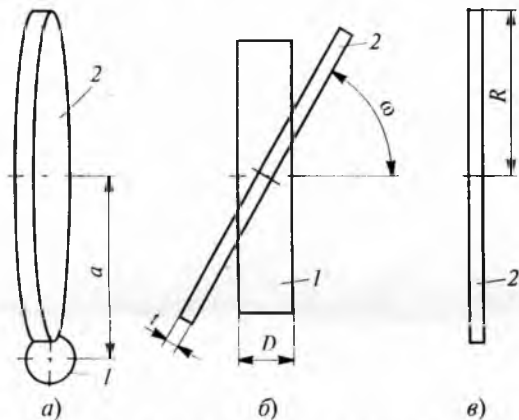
Схема обработки канавки: a — взаимное расположение заготовки 1 и ШК 2; b — вид сверху относительного расположения заготовки 1 и ШК 2; c — ШК простого профиля (D — диаметр заготовки)
